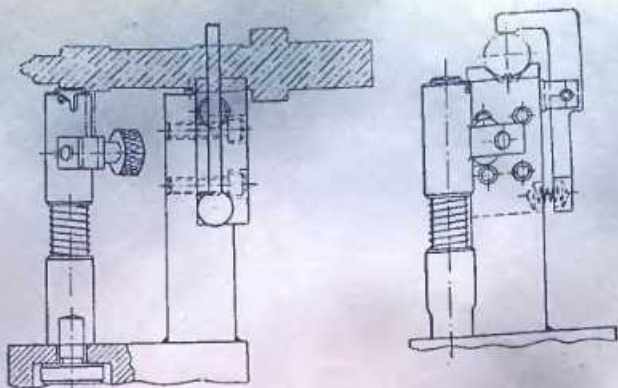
Приспособление ЛМ9579-436 для проверки биения распылителя и муфты на собранной форсунке
